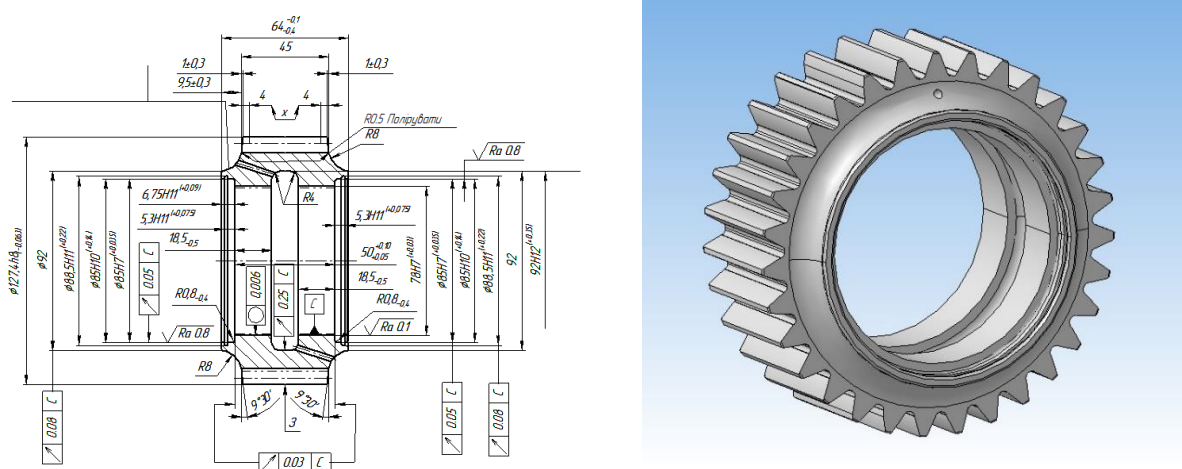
Креслення деталі «ШСП-12.12.23-01» та її 3D - модель
